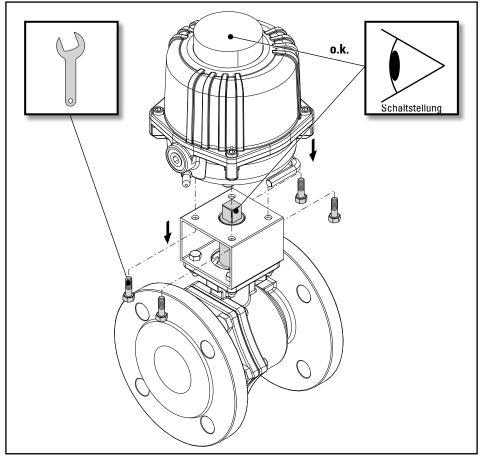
Einbau, Montage mittels Konsole und Spindel
